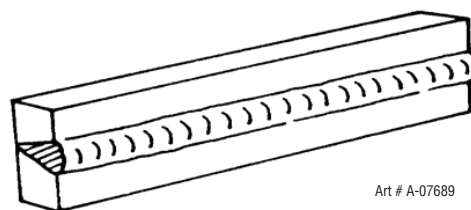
Posición horizontal, soldadura a tope
